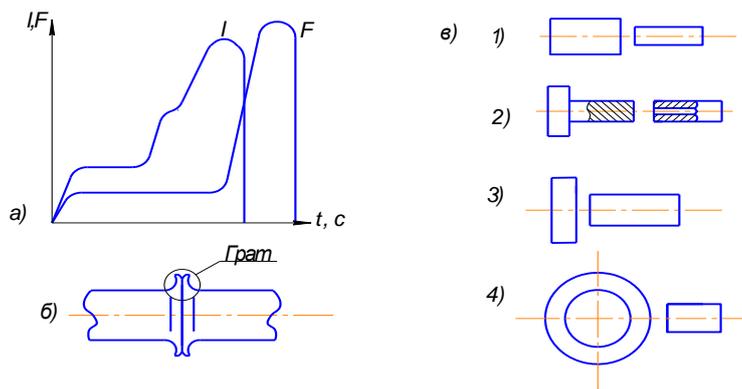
Схема контактной стыковой сварки оплавлением:
